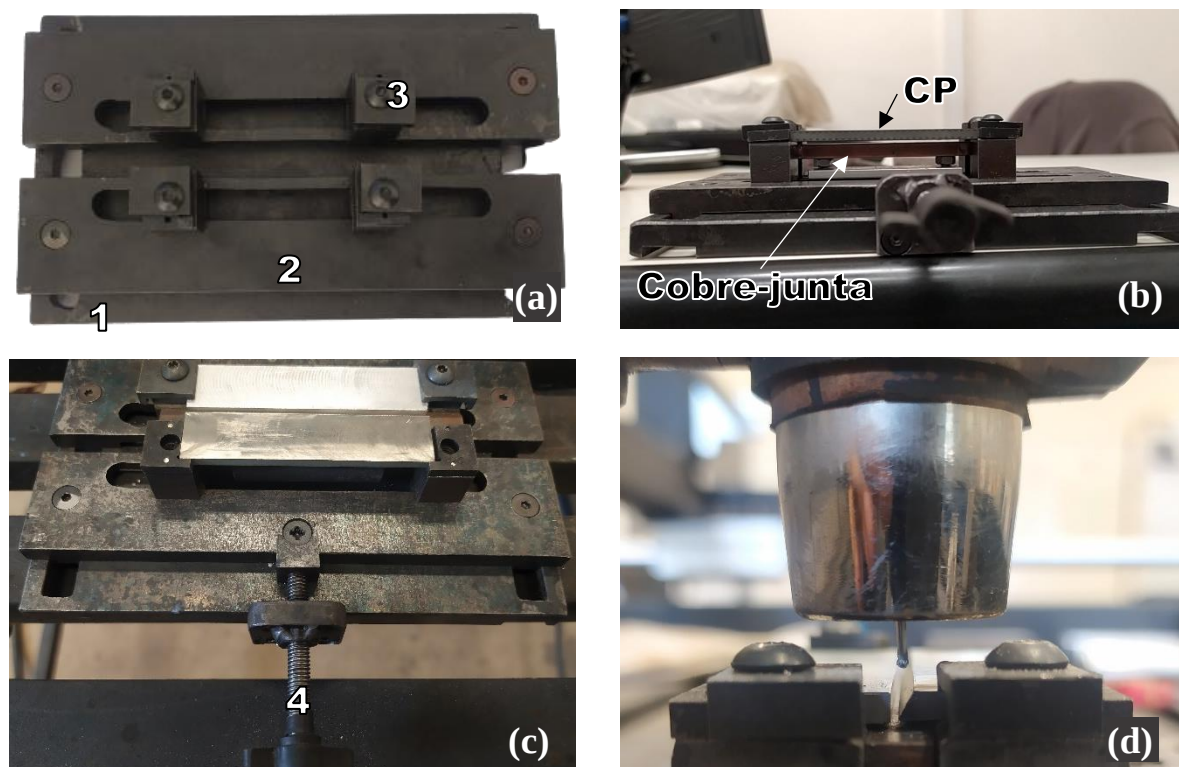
Dispositivo de fixação e ajuste da junta a ser soldada.
